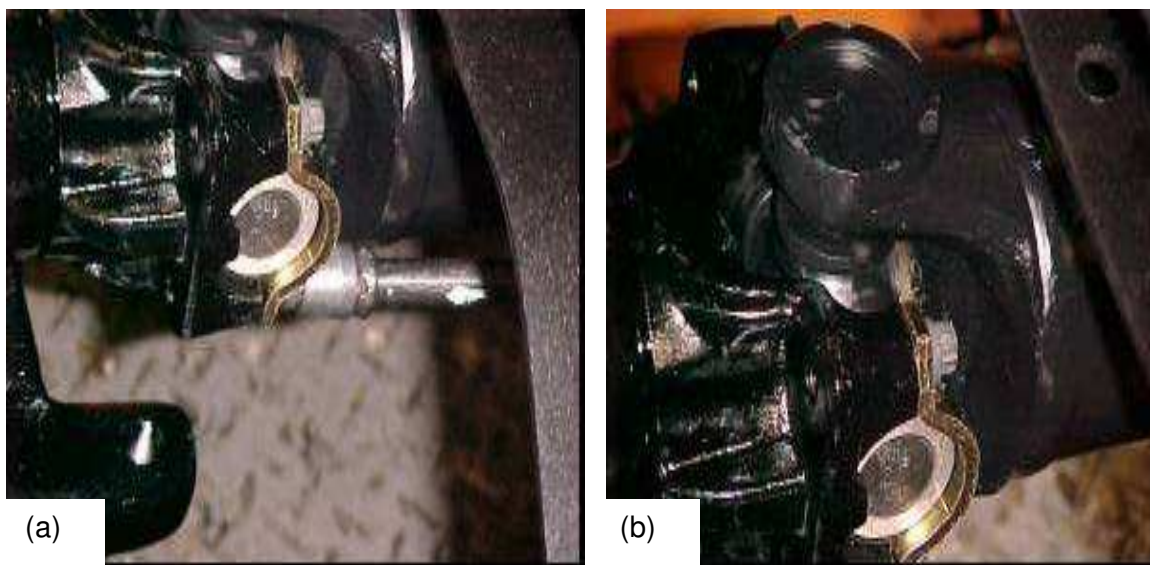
(a) Fixação do cardan (b) Cardan fixado
